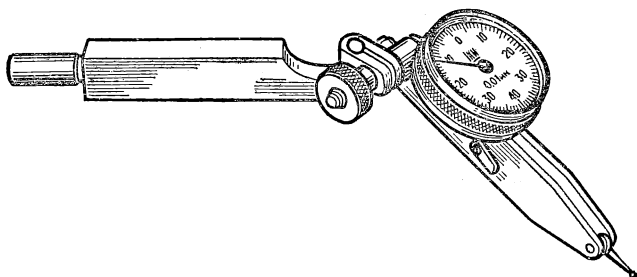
Малогабаритный рычажно-зубчатый индикатор
